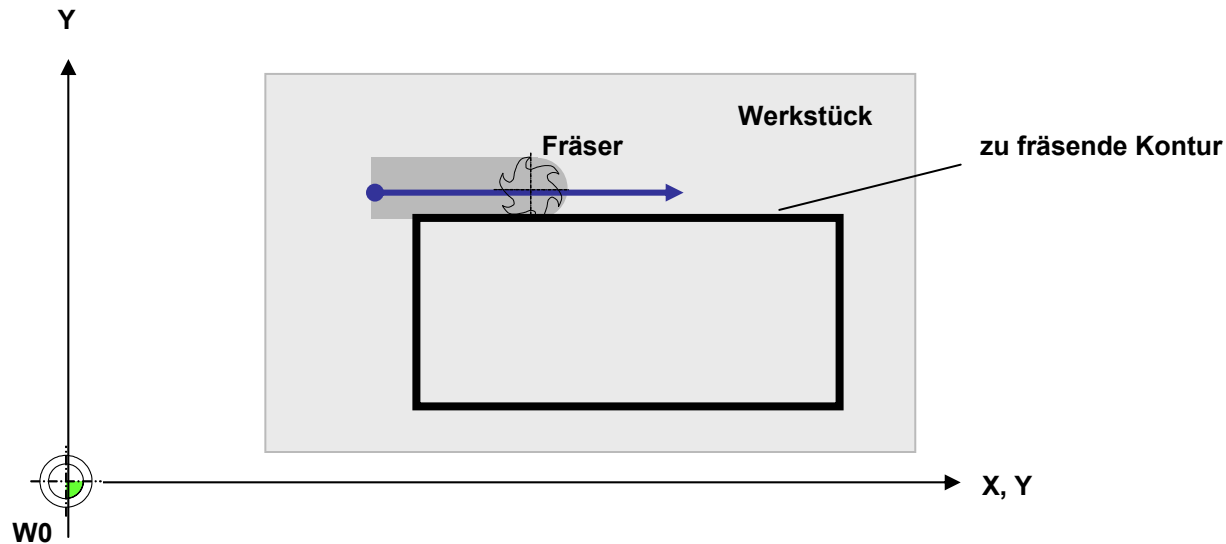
Beispiel für eingeschaltete Fräserradiuskorrektur
